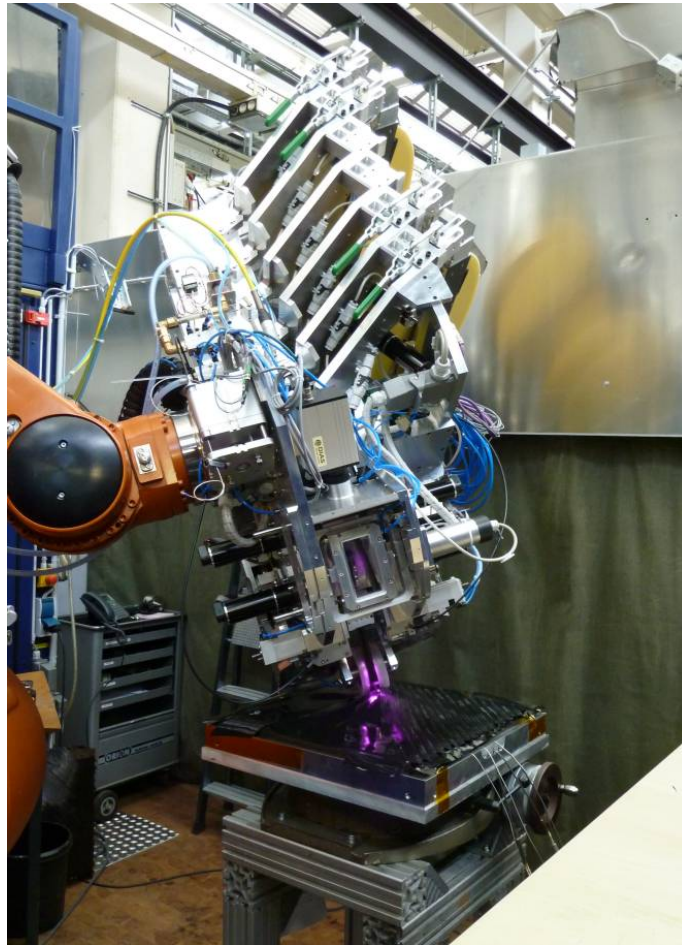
Bewegung des Tapelegekopfs auf dem 3D-Werkzeug mittels CAD/CAM-Unterstützung
